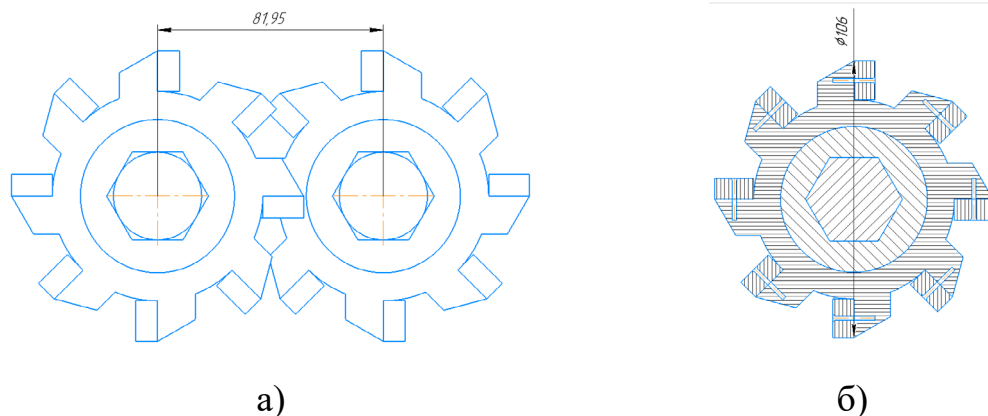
Расчет наружного диаметра корпуса ножа
